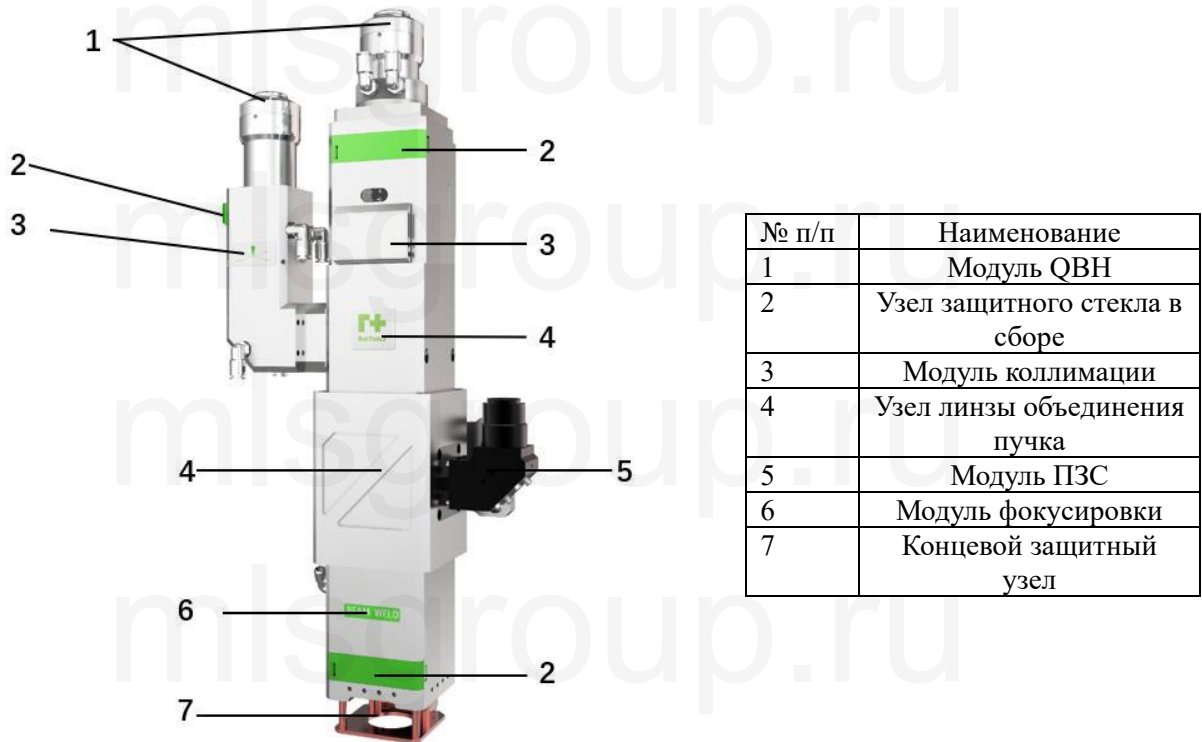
Схема конструкции лазерной сварочной головки с двойным диапазоном BW290
